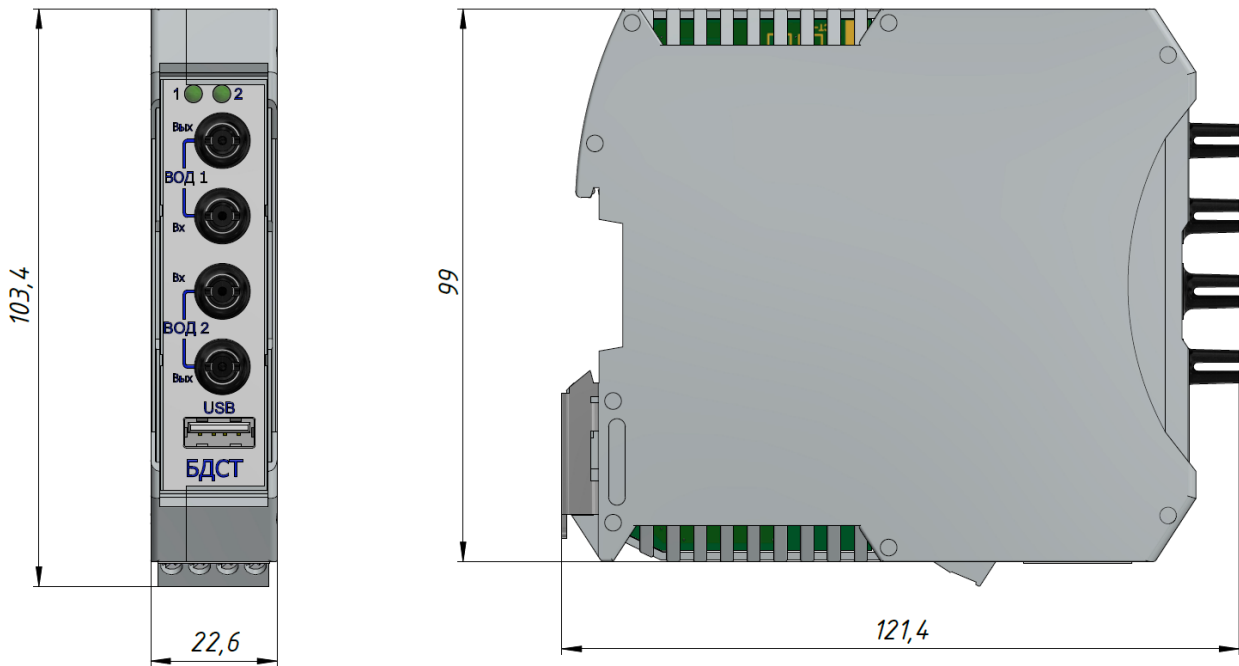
Внешний вид и габаритные размеры БДСТ
